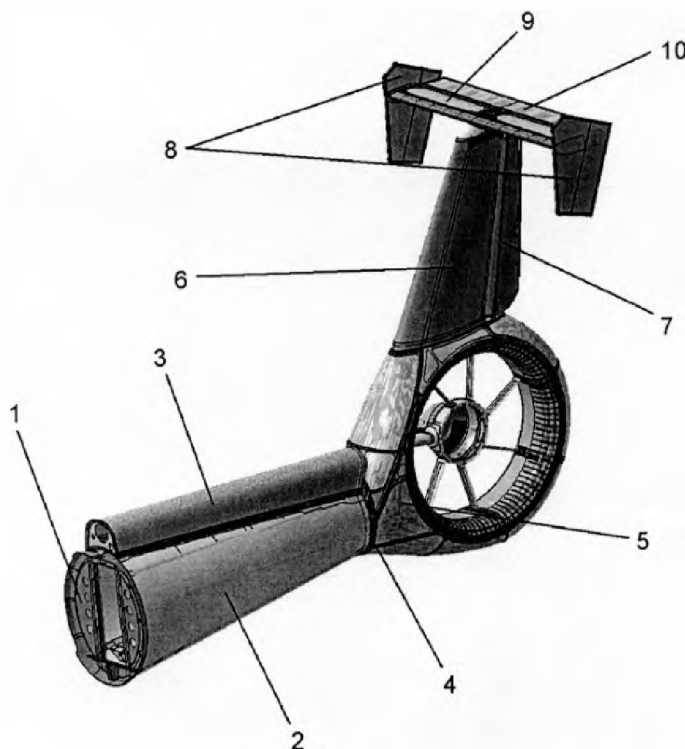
Конструкция хвостовой балки с оперением вертолета Ка-60/62 [20]:
